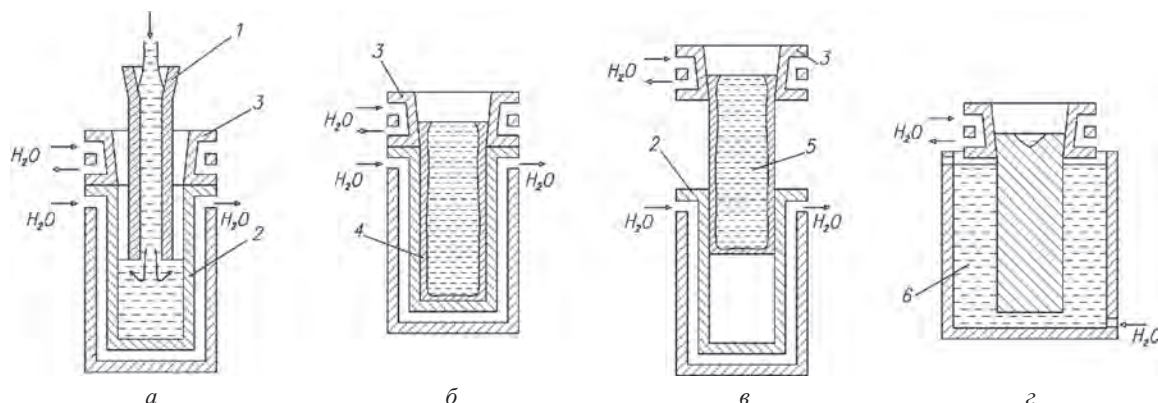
Схема литья закалочным затвердеванием: а — заполнение кристаллизатора; б — формирование стакана; в — извлечение стакана с расплавом; г — закалочное затвердевание — получение отливки: 1 — заливочное устройство; 2 — стационарный кристаллизатор; 3 — подвижный кристаллизатор; 4 — стакан; 5 — расплав; 6 — закалочная ванна
